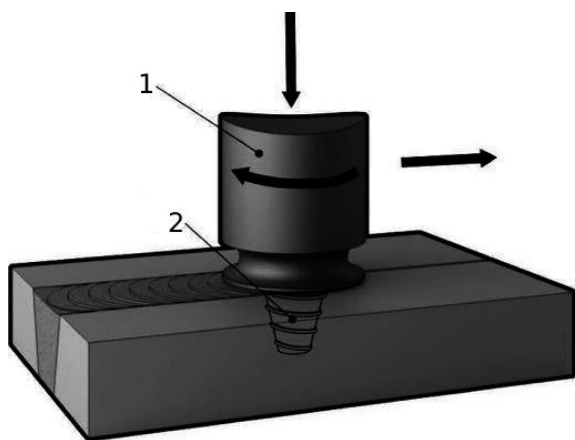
Схема процесу зварювання тертям з перемішуванням; 1 – обмежувальник; 2 – робоча частина інструмента
